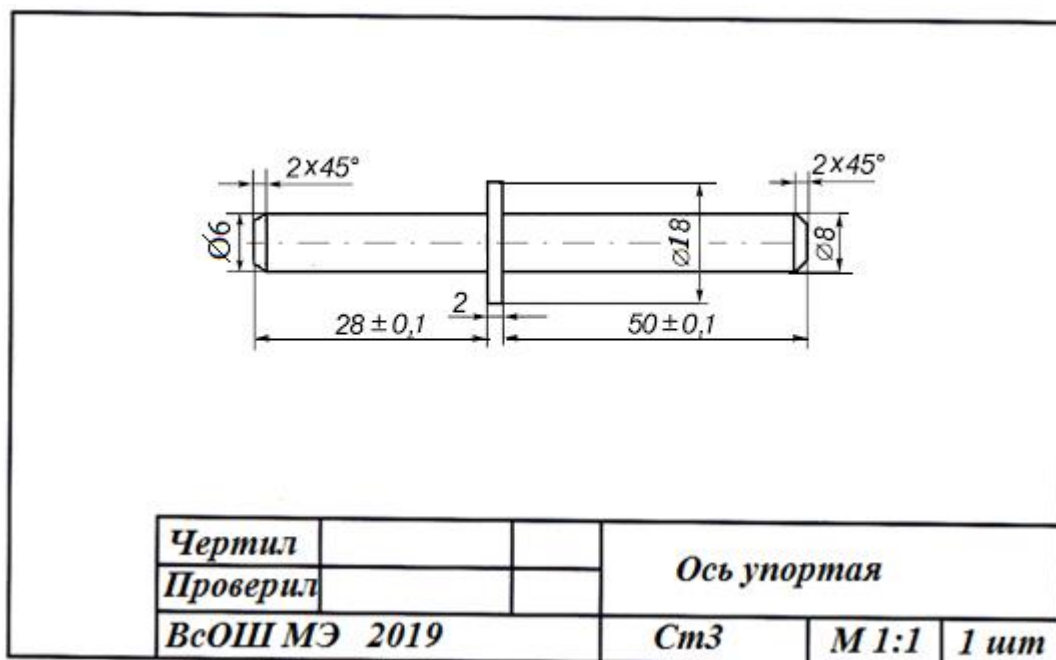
Чертёж образца для учебного измерения штангенциркулем – ось упорная
